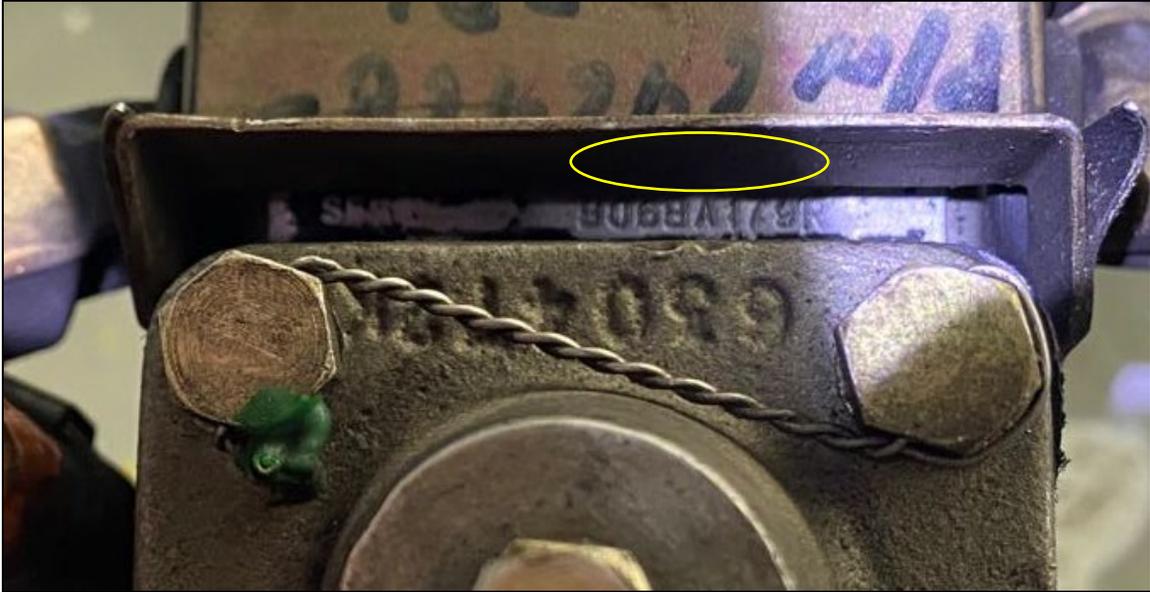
Bomba de combustible encontrada en la inspección del motor P/N: 646768-3A1 S/N: BO6BA179R
